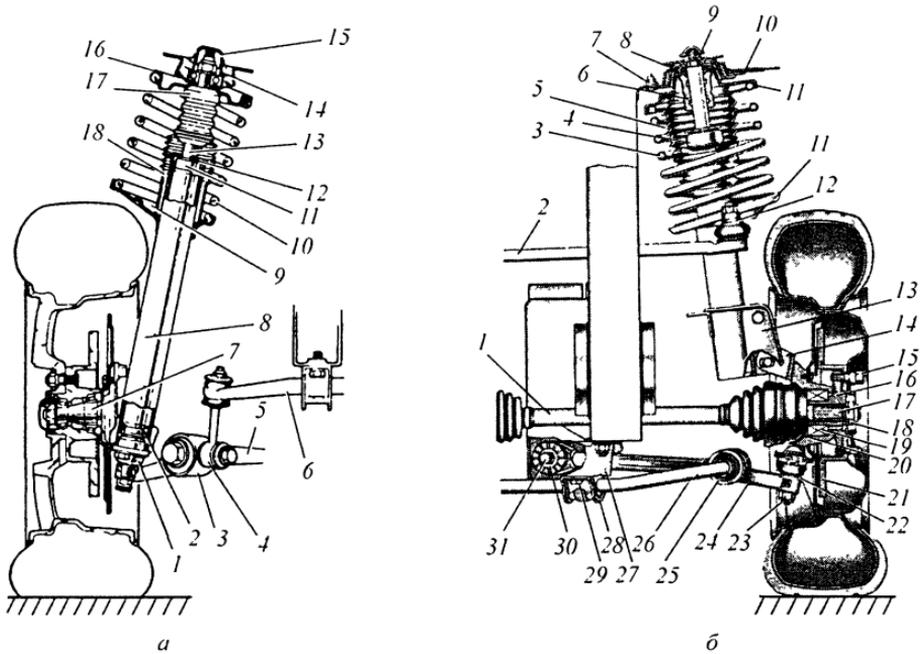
Подвеска типа Макферсон: *а* — пружинная стойка неведущего моста: 1 — шаровой шарнир управляющего рычага; 2 — седло амортизатора; 3 — управляющий рычаг; 4 — стойка стабилизатора поперечной устойчивости; 5 — толкающая штанга; 6 — стабилизатор поперечной устойчивости; 7 — поворотная цапфа; 8 — трубка стойки; 9 — нижнее гнездо пружины; 10 — пружина; 11 — амортизатор; 12 — крепежная гайка амортизатора; 13 — поршневой шток; 14 — верхнее крепление; 15 — крышка; 16 — верхнее гнездо пружины; 17 — жесткий упор; 18 — гофрированная трубка (сильфом); *б* — пружинная стойка ведущего моста: 1 — вал привода ведущих колес; 2 — наружный наконечник рулевой тяги; 3 — пружина подвески; 4 — амортизаторная (телескопическая) стойка; 5 — защитный чехол; 6 — буфер сжатия; 7 — самоподпорящаяся гайка; 8 — упорный подшипник стойки; 9 — гайка крепления стойки; 10 — верхняя опора стойки; 11 — опорные чашки пружины; 12 — поворотный рычаг; 13 — скоба резервуара амортизаторной стойки; 14 — поворотный кулак; 15 — болт крепления диска колеса; 16 — ступица переднего колеса; 17 — шлицевой хвостовик корпуса наружного шарнира; 18 — гайка ступицы; 19 — подшипник колеса; 20 — стопорное кольцо подшипника; 21 — тормозной диск; 22 — шаровая опора; 23 — гайка шаровой опоры; 24 — рычаг подвески; 25 — шарнир; 26 — штанга стабилизатора поперечной устойчивости; 27 — поперечина передней опоры двигателя; 28 — обойма штанги стабилизатора; 29 — болт крепления обоймы; 30 — резинометаллический шарнир; 31 — болт крепления шарнира
